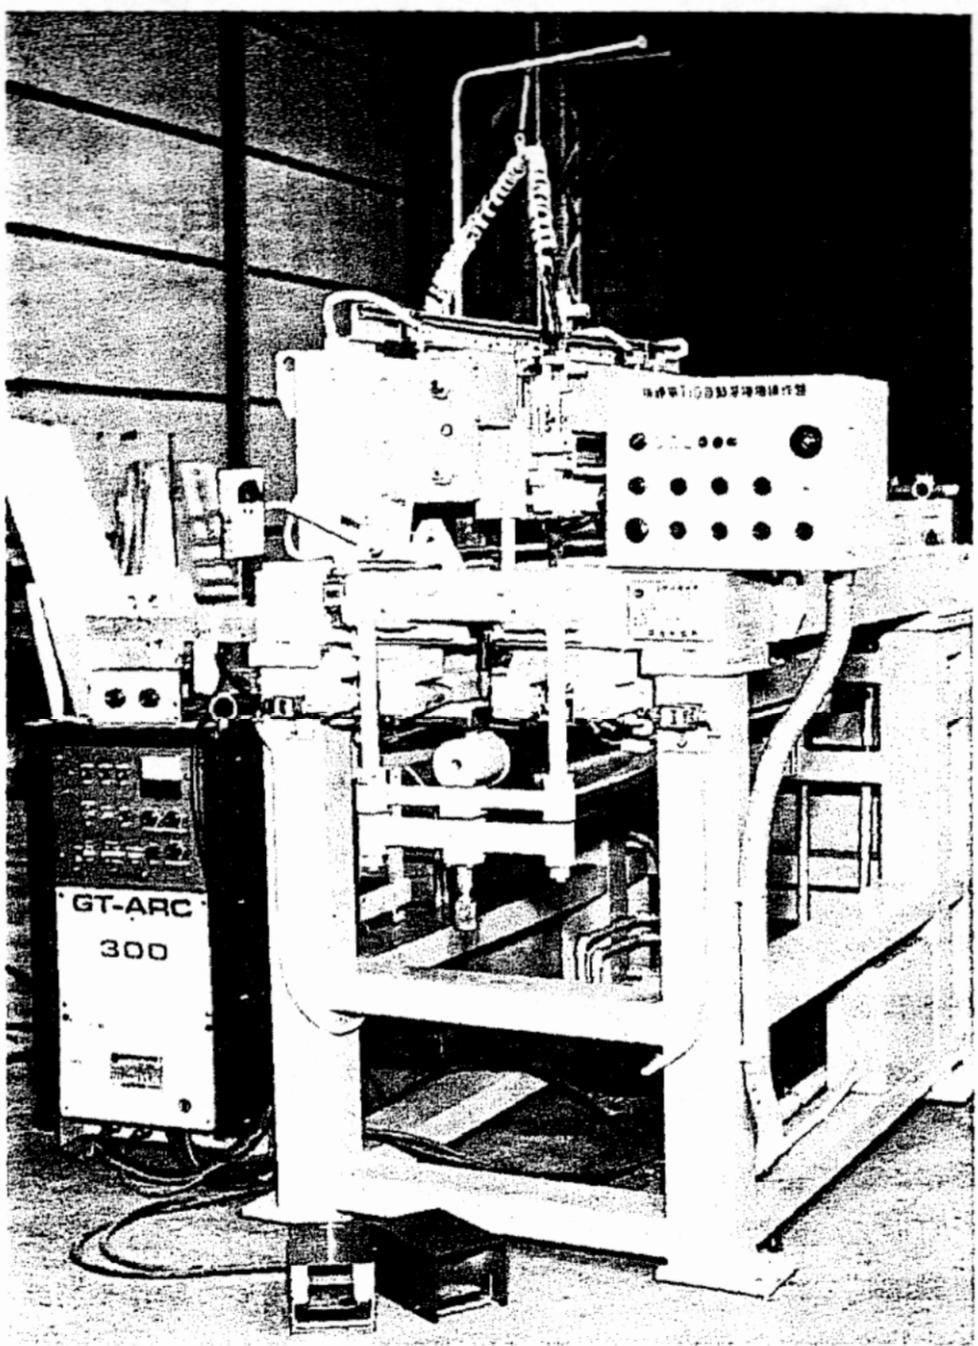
Автомат длястыковой сварки продольного соединения цилиндра
